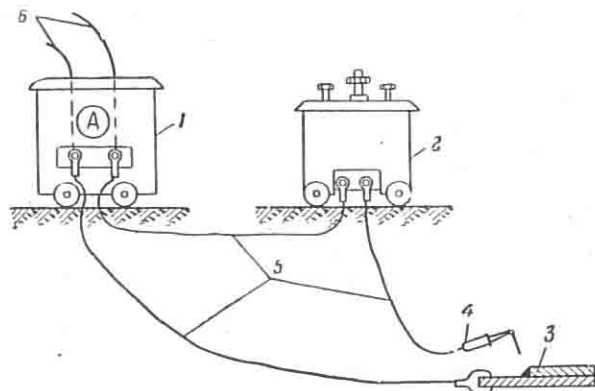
Схема сварочной трансформаторной установки СТЭ-34: 1 — трансформатор; 2 — регулятор силы сварочного тока; 3 — свариваемые детали; 4 — электродержатель; 5 — сварочные провода; 6 — провода силовой сети
